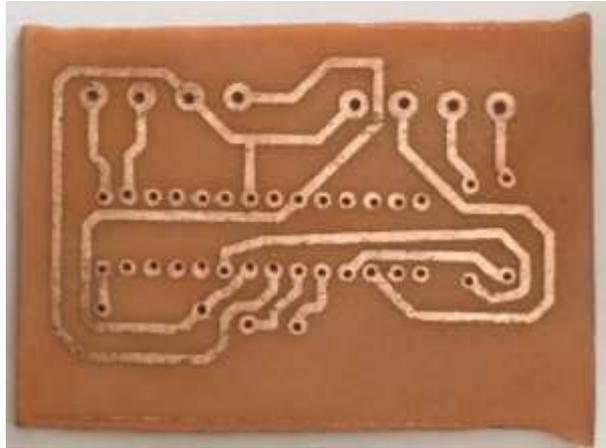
Diagrama de pistas impresa de la PCB diseñada
